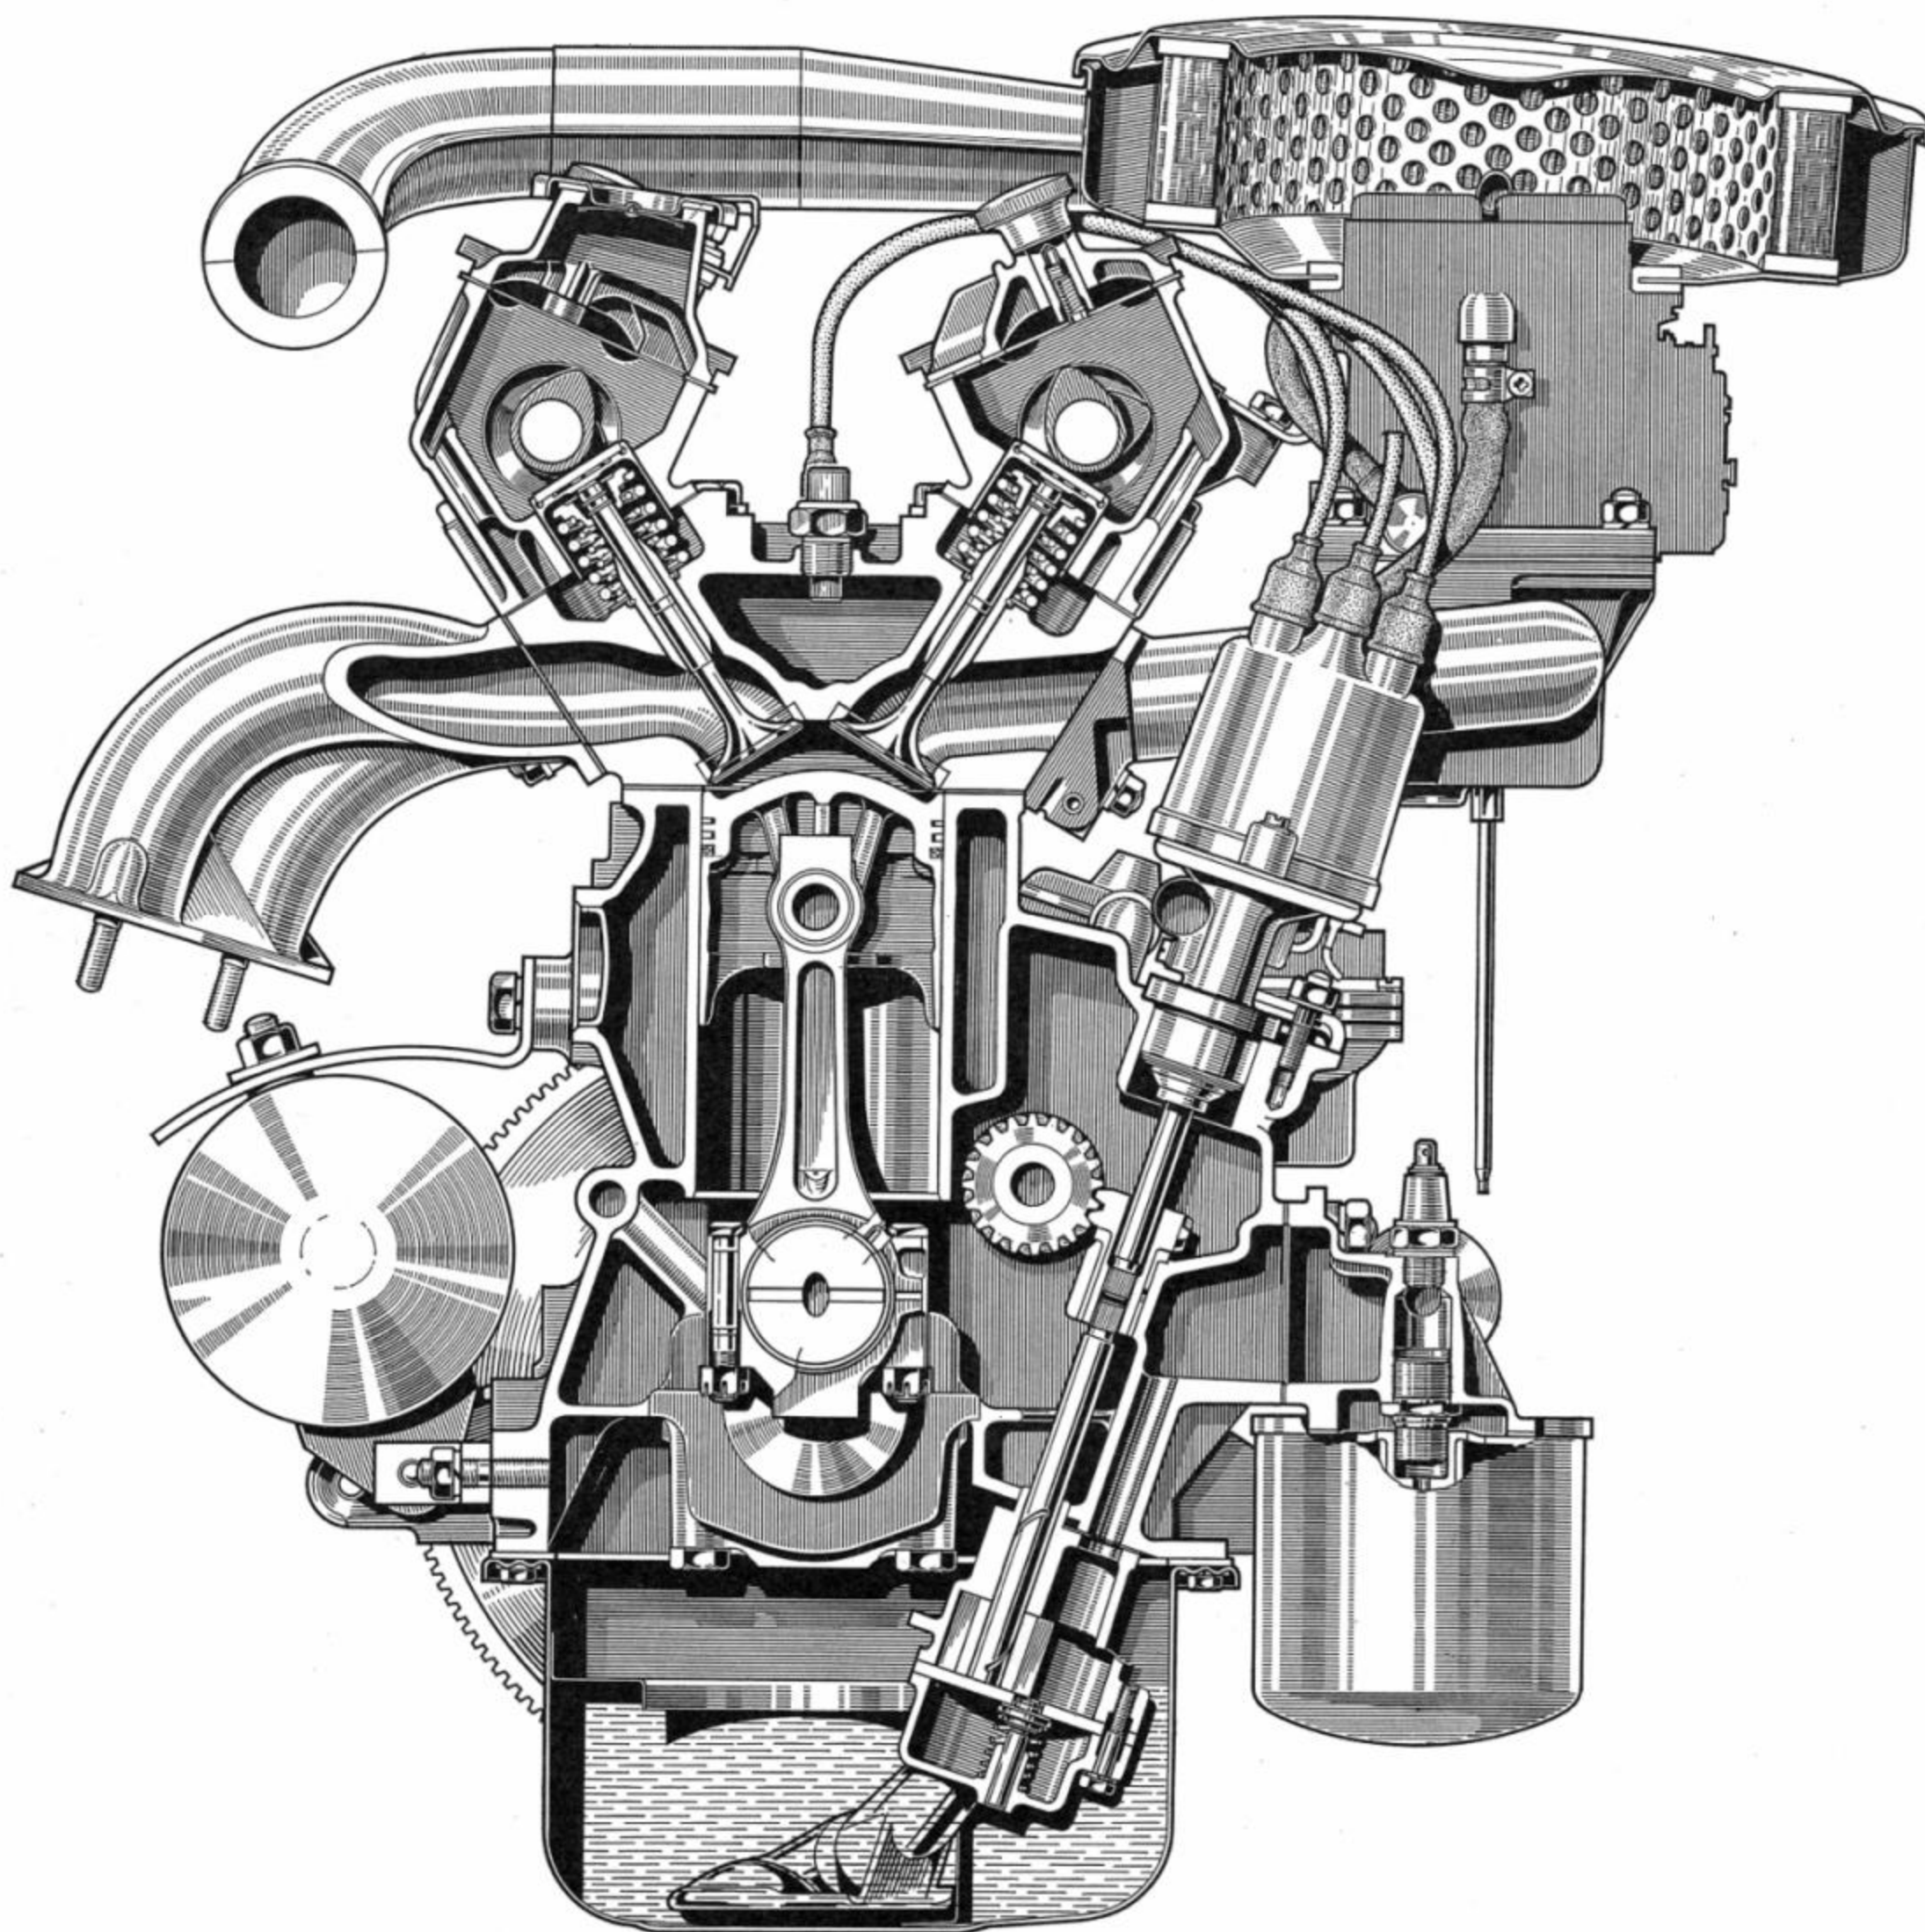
Querschnitt durch die Zylinder und die Ventile des Motors.
